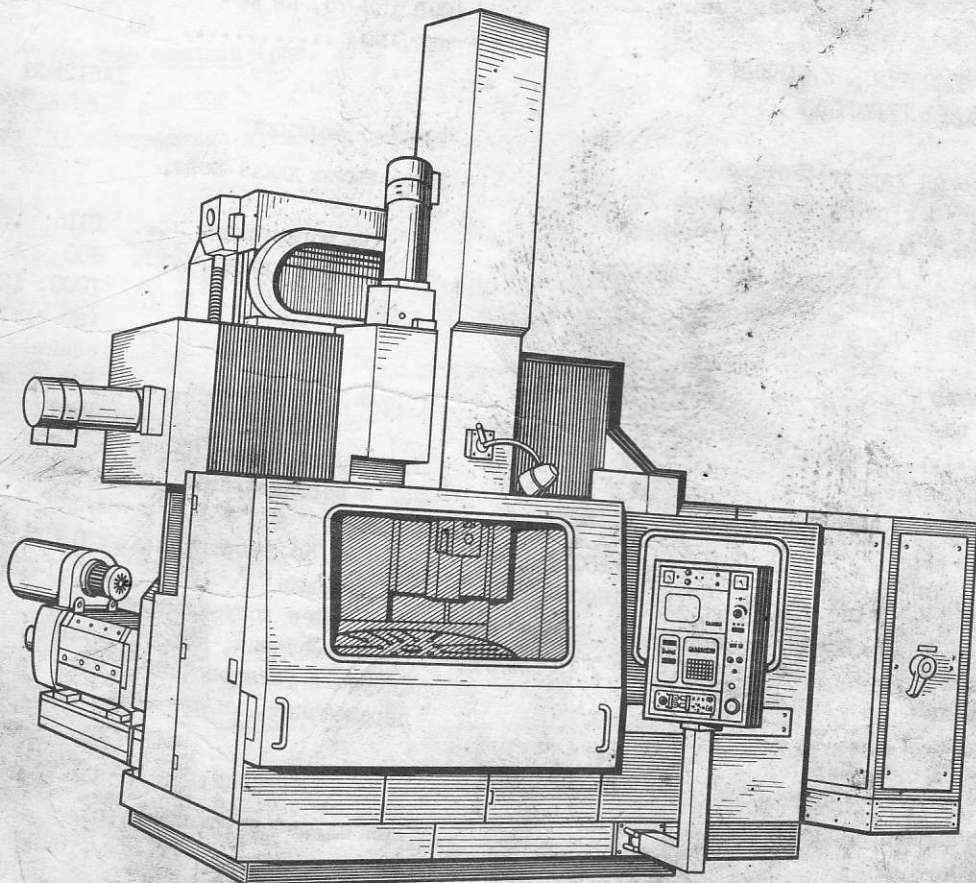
Рис. I. Станок токарно-карусельный одностоечный с ЧПУ
